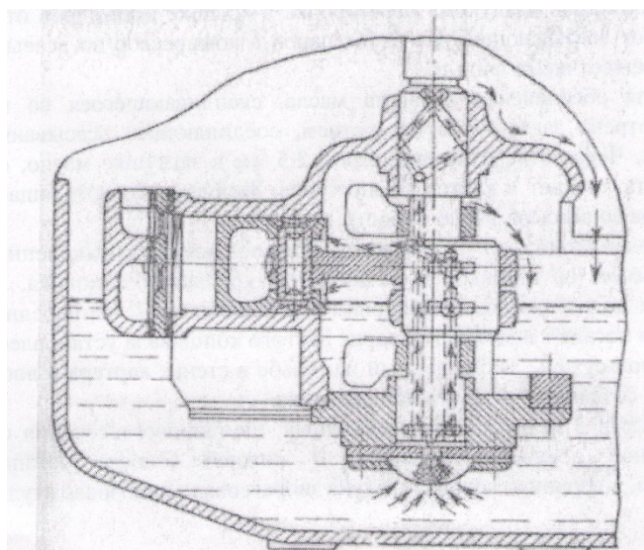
Схема смазки герметичного компрессора ФГ-0,7~3
